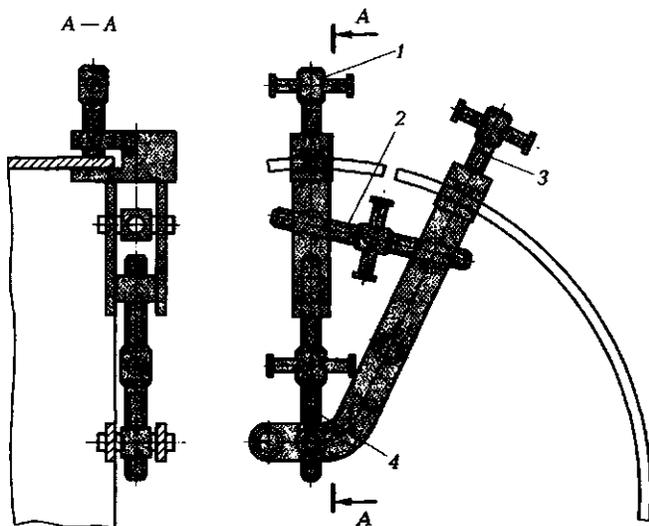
Стяжка для сборки продольного стыка обечайки:
